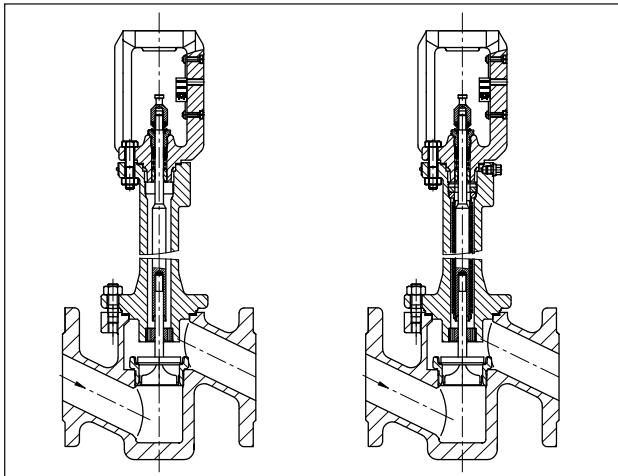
Ventil Typ 3241 · DN 15 bis 80 · Schmiedestahlausführung · links: mit Isolierteil, rechts: mit Balgeabdichtung
